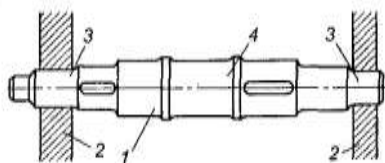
Прямой вал: 1 — вал; 2 — опоры вала; 3 — цапфы; 4 — шейка
